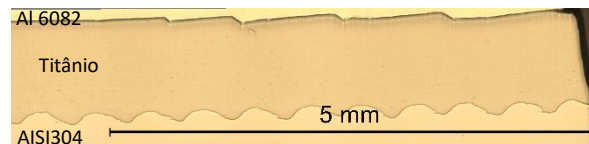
Macrografia das interfaces da soldadura Al-Ti-AISI304.
